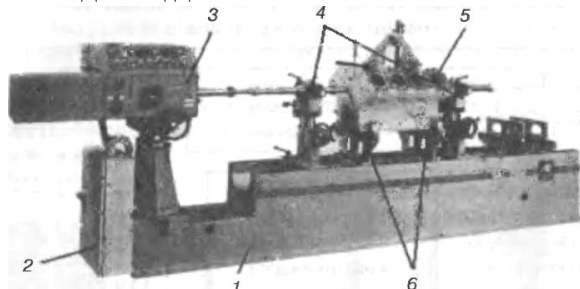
Горизонтально-расточной станок ВАС 1500 для обработки постелей коленчатых и распределительных валов двигателей легковых автомобилей фирмы AZ MACHING TOOLS (Италия): 1 — станина; 2 — блок питания; 3 — передняя бабка; 4 — регулируемые опоры борштанги; 5 — блок цилиндров; 6 — опоры для установки изделия
